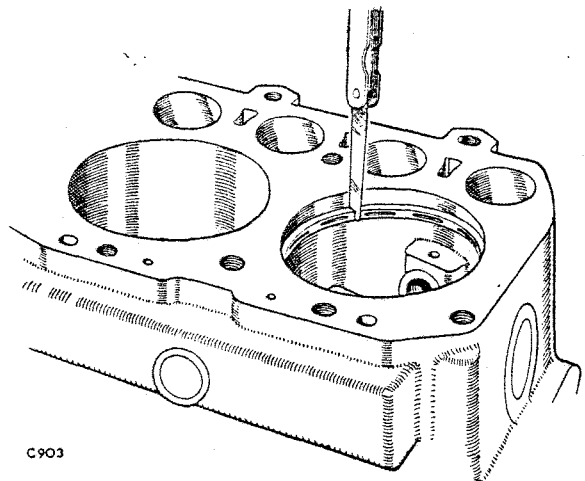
Comprobación de la tolerancia del aro de pistón.
